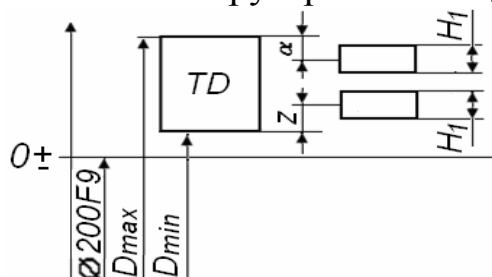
Схема розташування полів допусків калібру-пробки.
